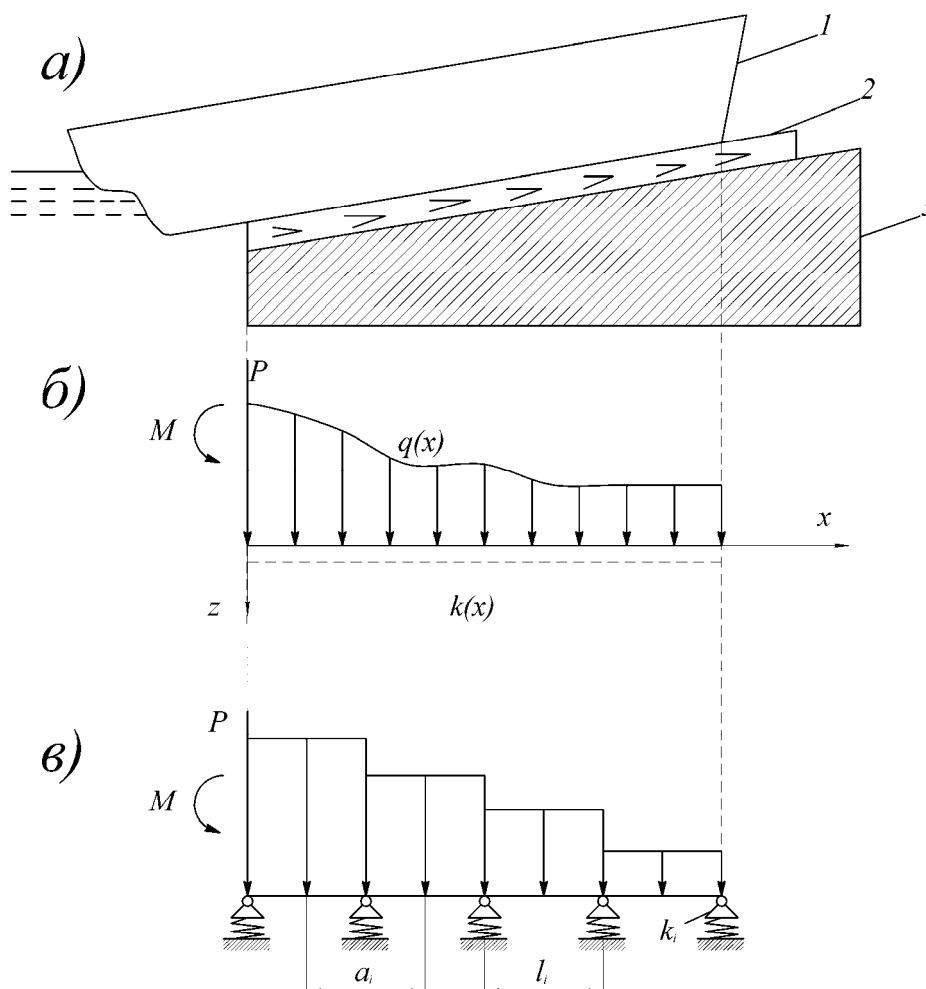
Розрахункова схема оцінки загального згину корпусу судна-балки при спусканні з поздовжнього стапелю: 1 – корпус судна-балки; 2 – спусковий пристрій; 3 – стапельна площина для спускового пристрою
